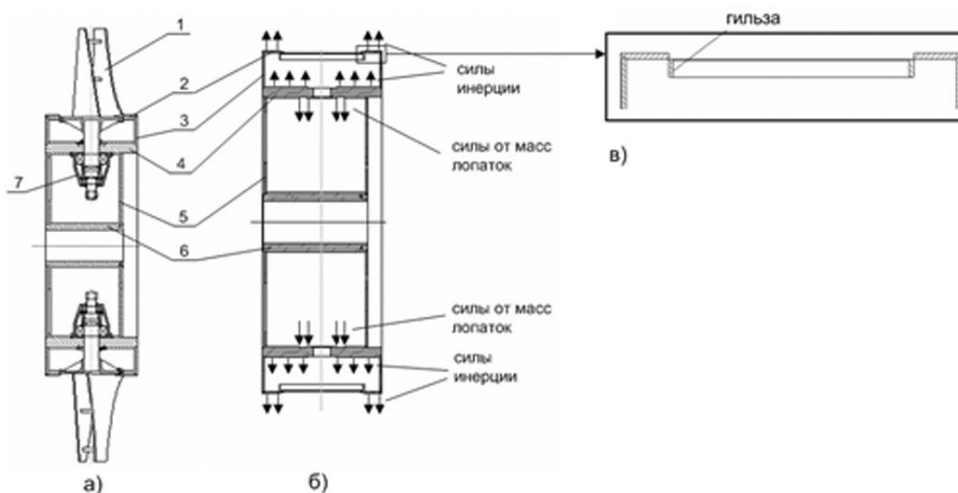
Рабочее колесо: а) схема рабочего колеса вентилятора; б) силы, действующие на рабочее колесо; в) гильза в корпусе рабочего колеса: 1 – сдвоенная листовая лопатка, 2 – обечайка, 3 – опорный диск, 4 – силовой пояс, 5 – несущий диск, 6 – ступица, 7 – стакан
